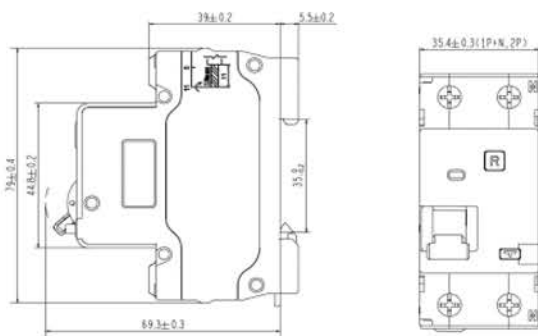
Установочные и габаритные размеры ДИФ-103 6кА 1P+N
